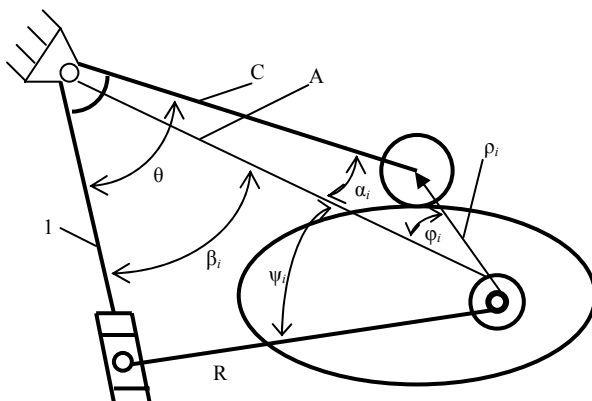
Расчетная схема кулачково-кулисного механизма для привода ремизок ткацких станков
